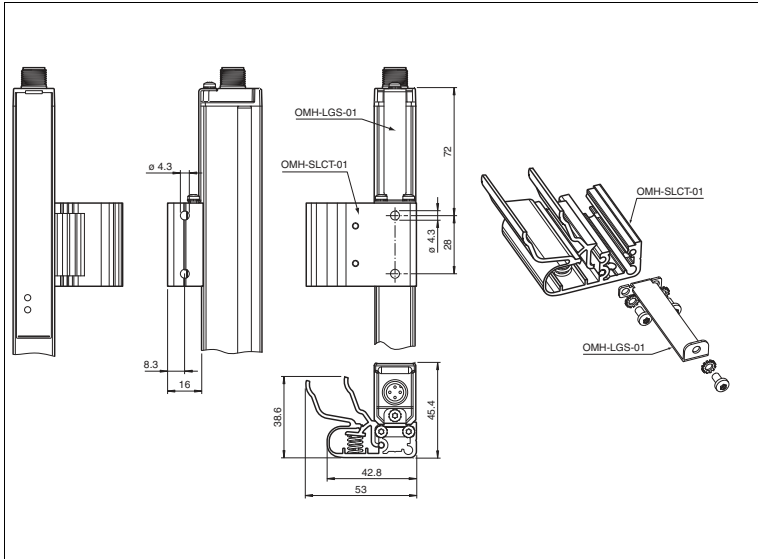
Abmessungszeichnung und Montage der Montagehilfe OMH-LGS-01
